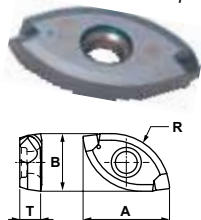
(для сварных швов и закаленных материалов)
